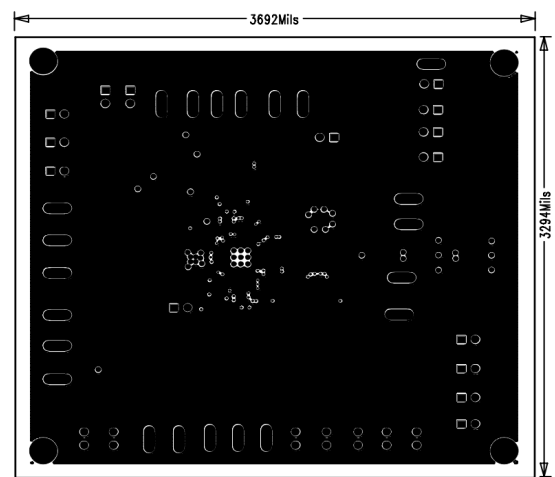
Max 8662 PCB LayOut - AGND Layer 4.
